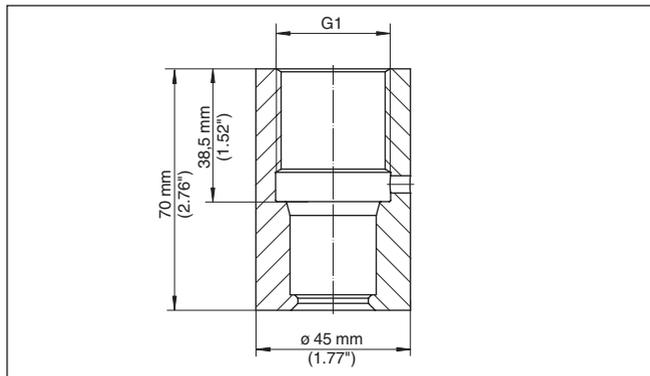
Dimensions raccord à souder G1 approprié pour PASVE (pour les deux versions répertoriées auparavant) - VEGABAR 82
